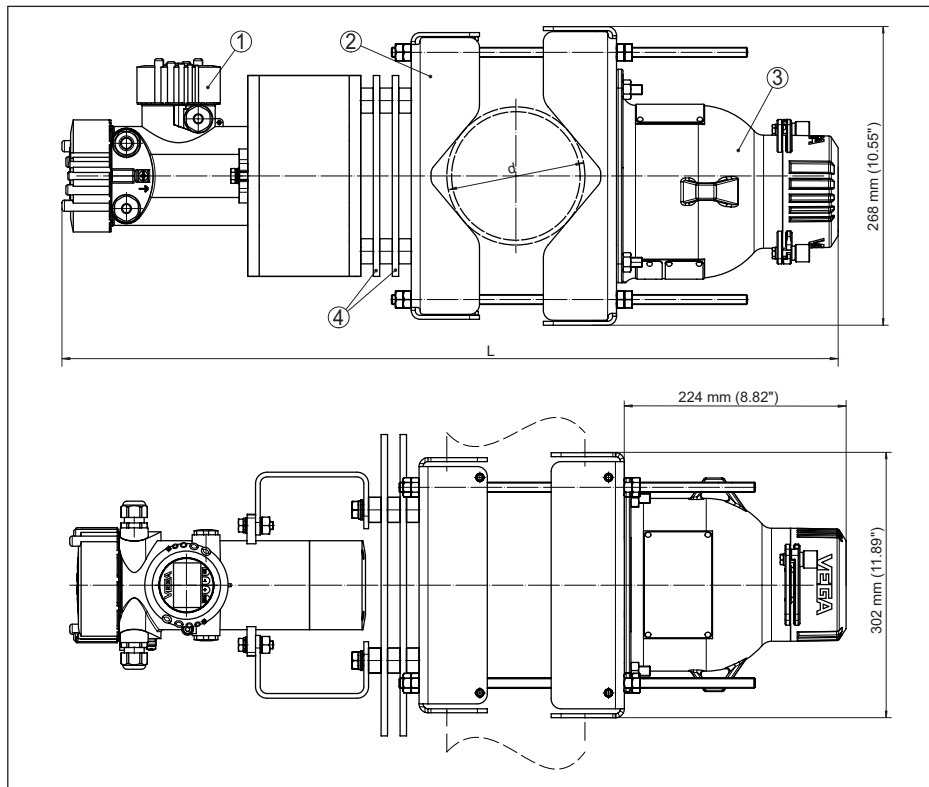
Dispositivo de sujeción con sensor montado horizontalmente y kit de protección térmica (con VEGA-SOURCE 81, 82, 83)
